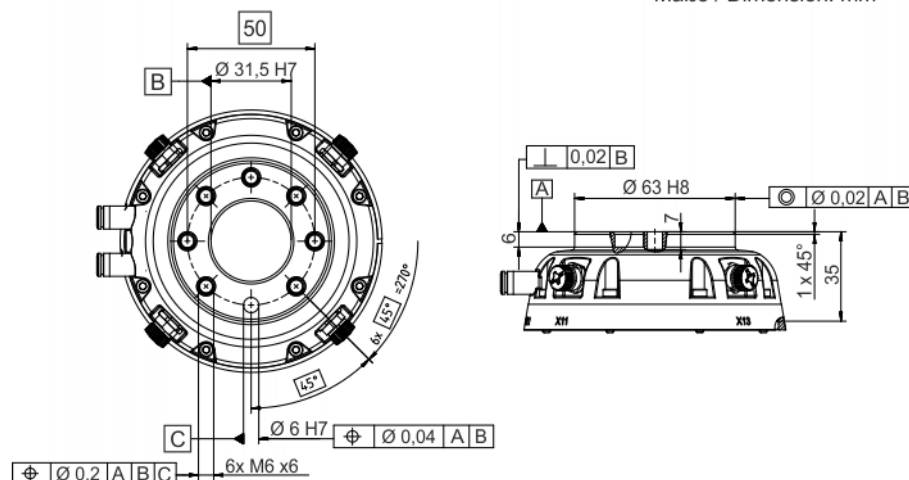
Abmessung, Medien-Flansch IO pneumatisch
